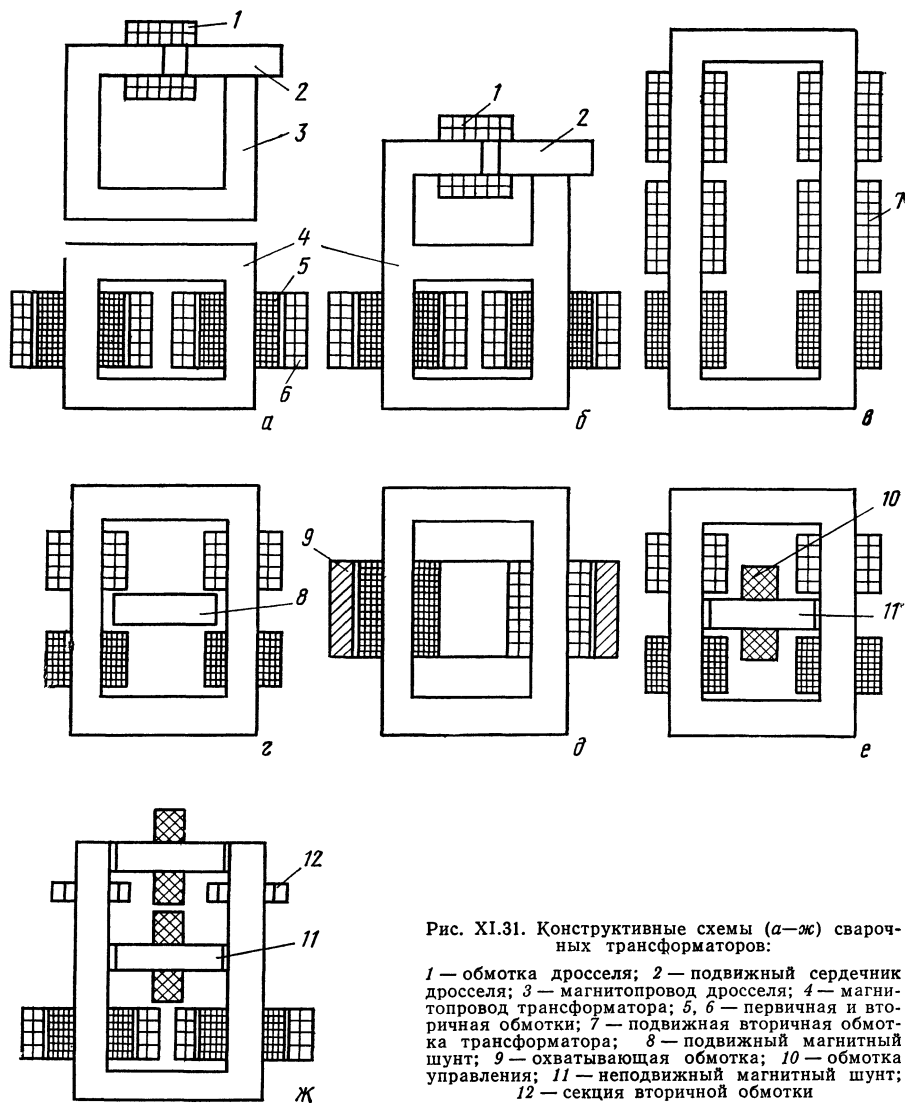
Конструктивные схемы (а-ж) сварочных трансформаторов:
